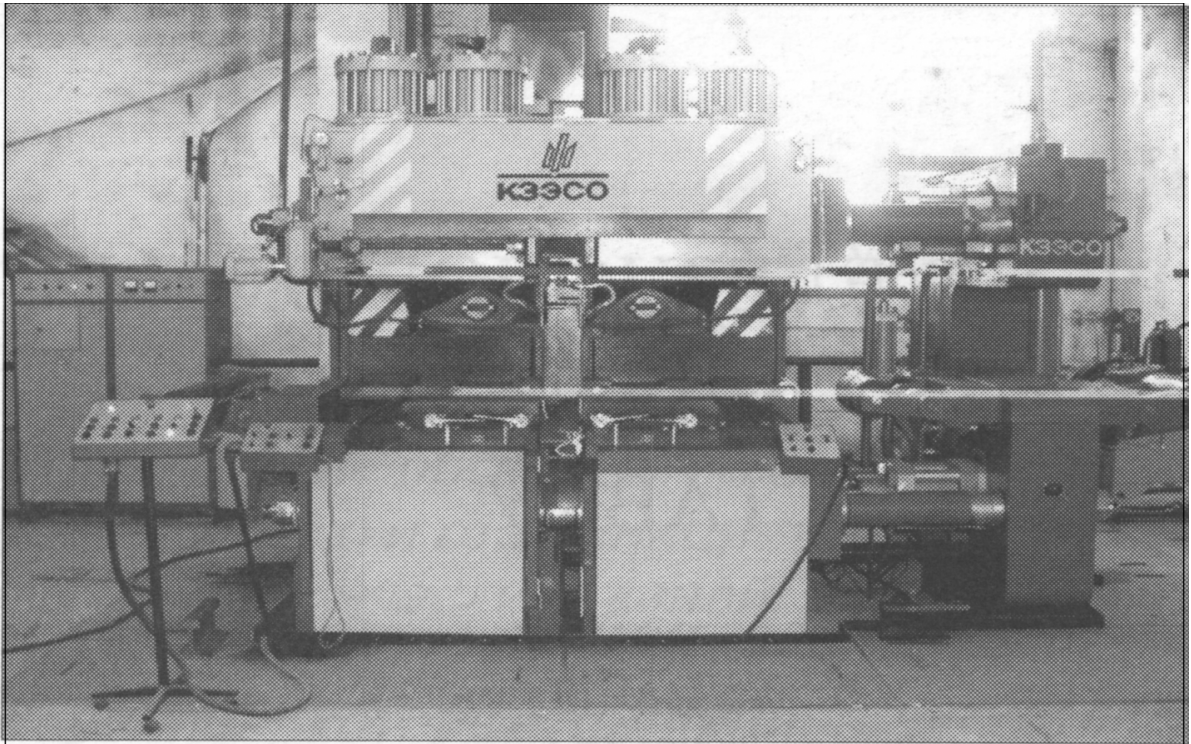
Загальний вигляд зварювальної машина K924M
